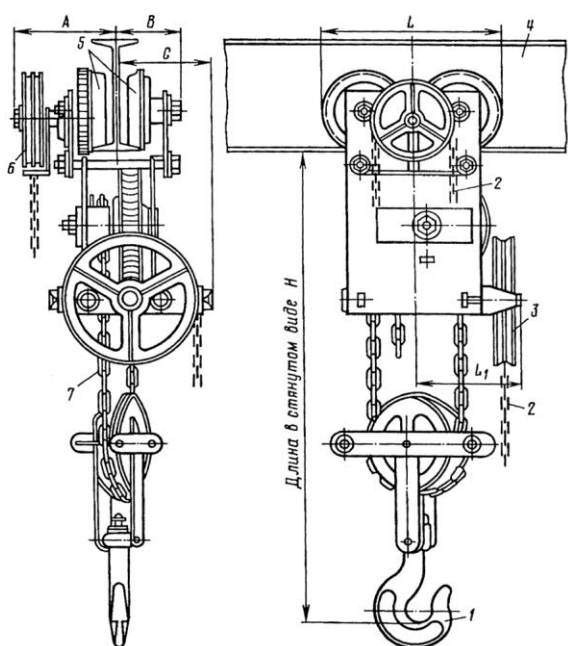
Схема ручной тали грузоподъемностью 1т: 1 – грузовой крюк; 2 – тяговые цепи; 3 – тяговое колесо подъемного механизма; 4 – двутавровая балка; 5 – ходовое колесо; 6 – колеса механизма передвижения; 7 – грузовая цепь
